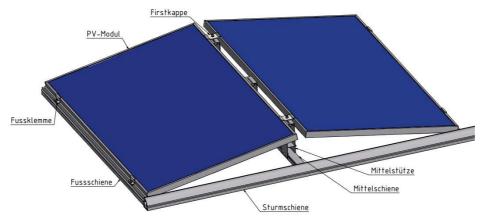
1-fach Element DUOFLAT, komplett montiert mit Sturmschiene
